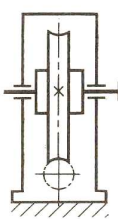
Червячный редуктор с верхним расположением червяка
